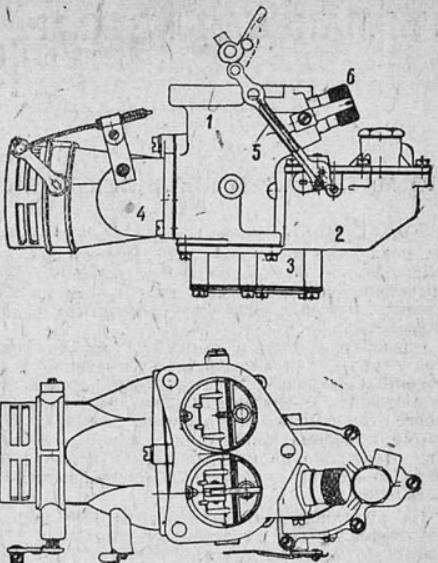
Общий вид карбюратора легкового автомобиля ЗИС.
